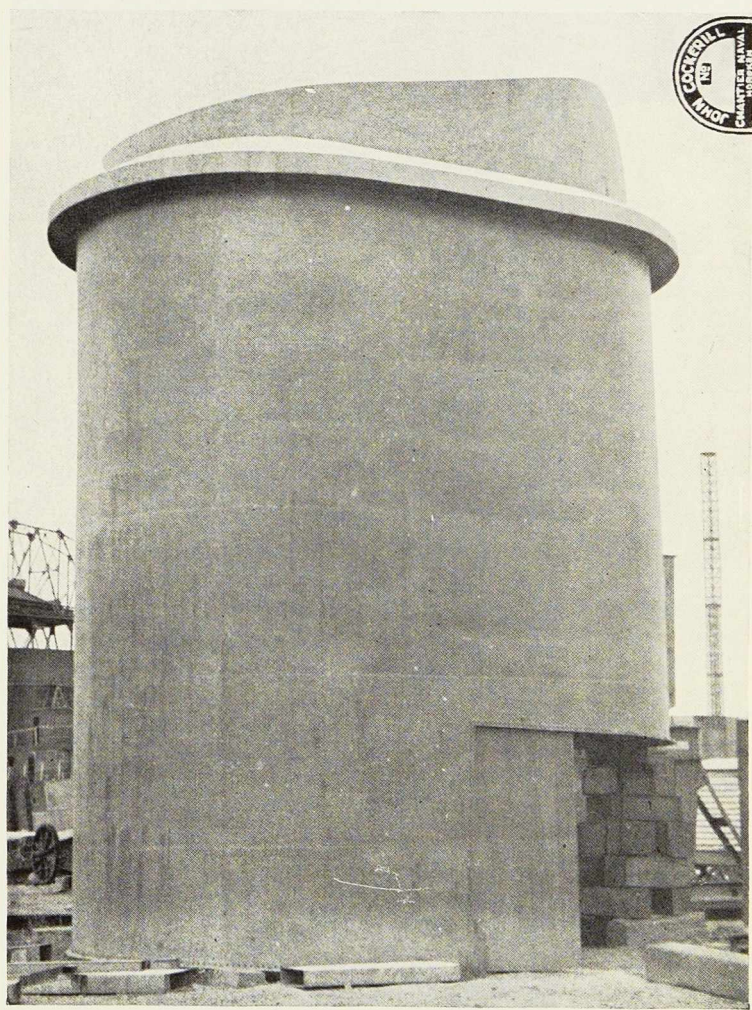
Cheminée de paquebot en construction soudée au chantier naval John Cockerill.
